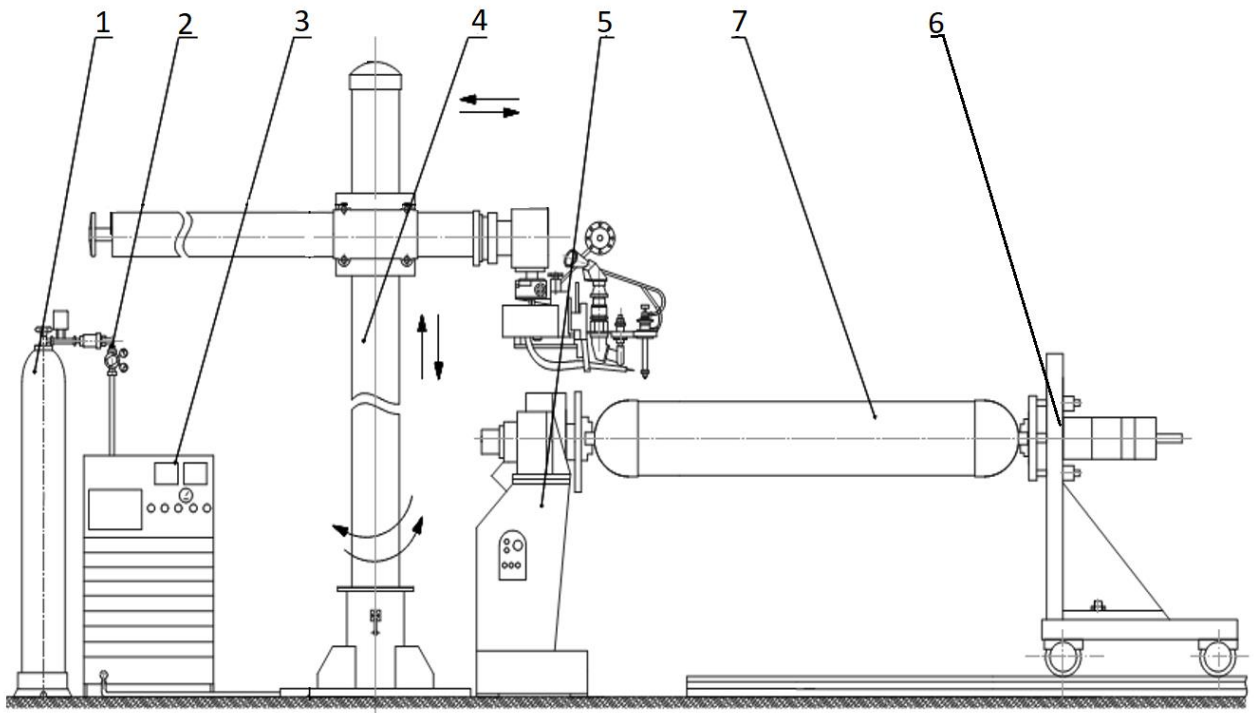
Установка для автоматичного зварювання повздовжніх та кільцевих швів
